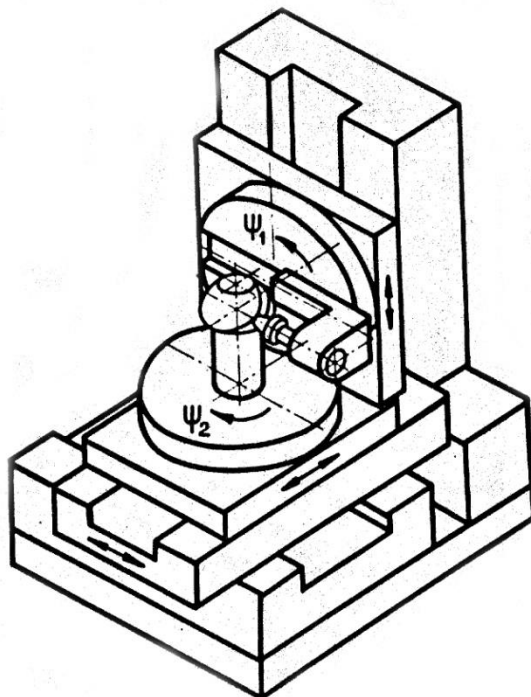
Компонка станка с ЧПУ, реализующего пятую кинематическую схему формообразования
